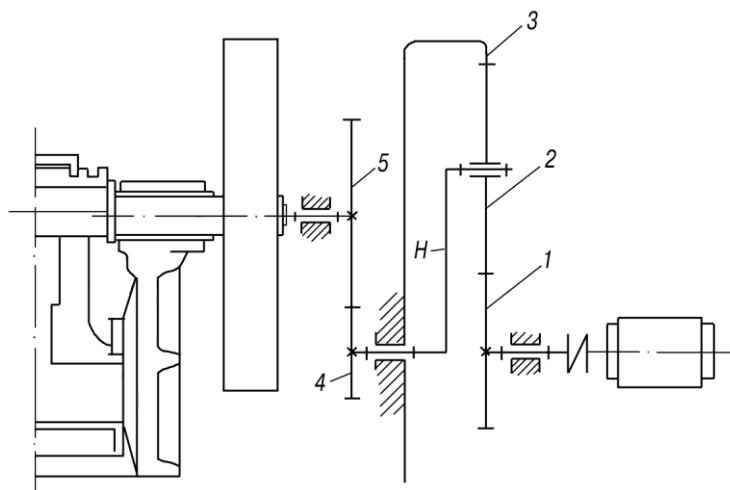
Механизм зубчатой передачи привода щековой дробилки
